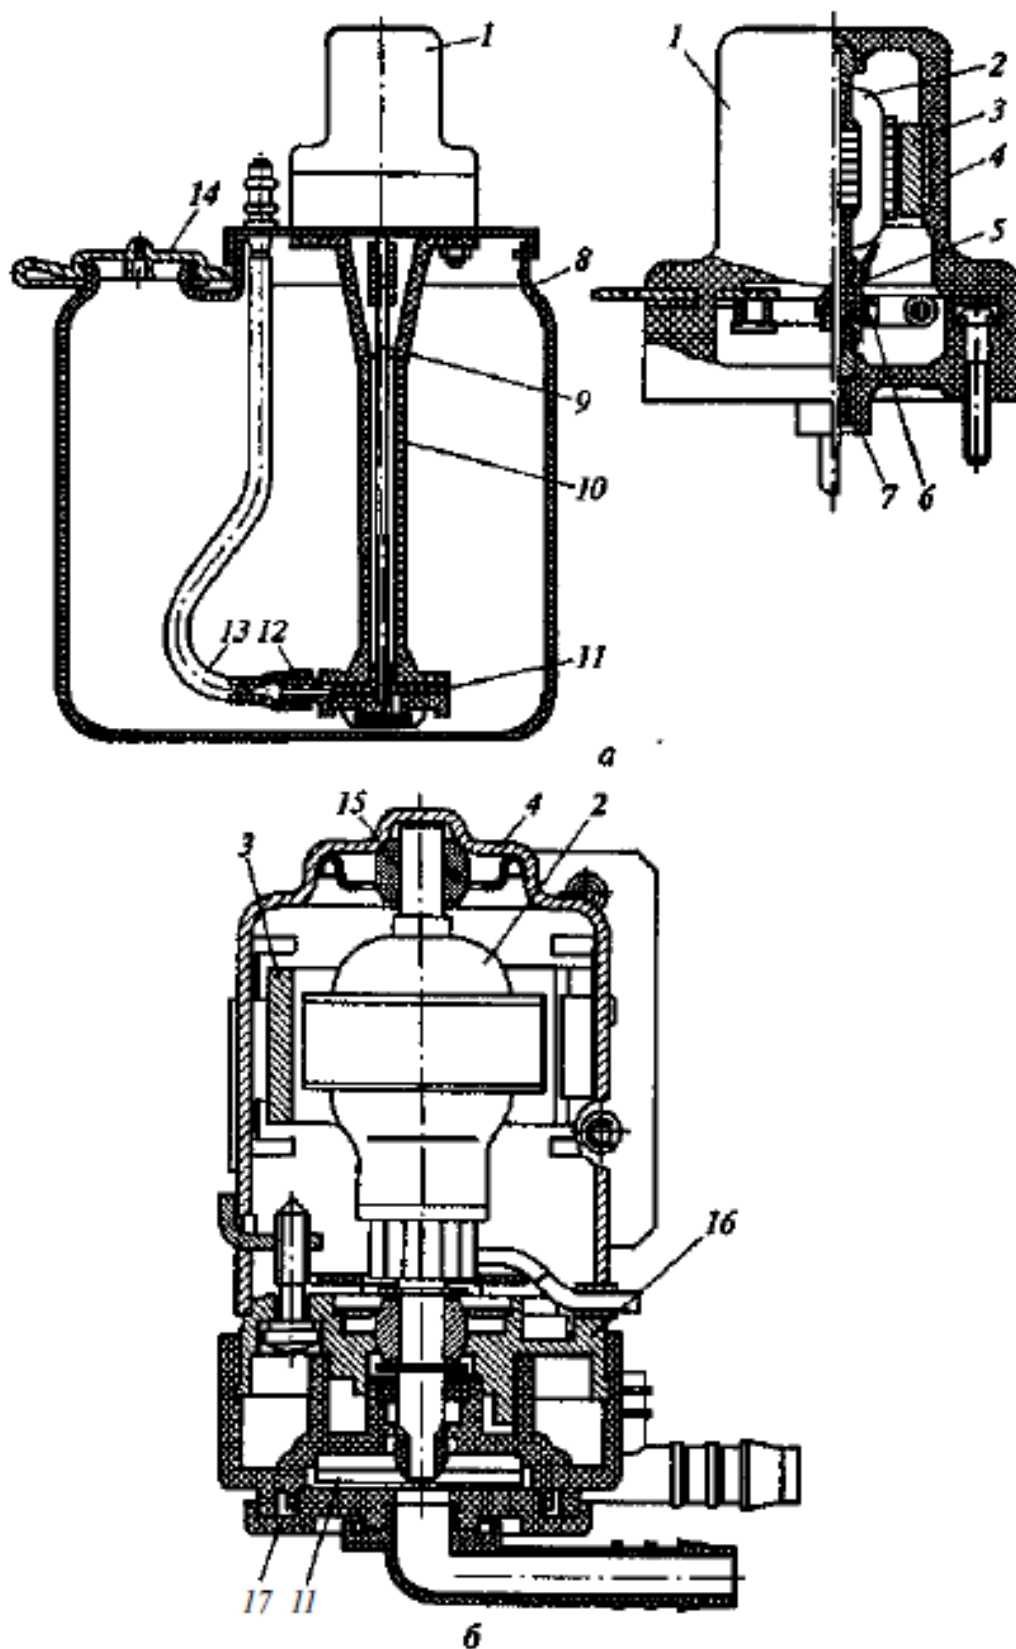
Насосное оборудование стеклоомывателей: а – для лобового стекла кузова (кабины); б – для фар; 1 –электронасос; 2 – якорь; 3 – постоянные магниты; 4 – корпус электродвигателя; 5 – коллектор; 6 – щетки; 7 – фланец; 8 – бачок; 9 – вал привода насоса; 10 – корпус насоса; 11 – ротор насоса (насосное колесо); 12 – штуцер; 13 – трубка; 14 – пробка горловины бачка; 15 – подшипник скольжения; 16 – корпус подшипника; 17 – крышка ротора насоса
